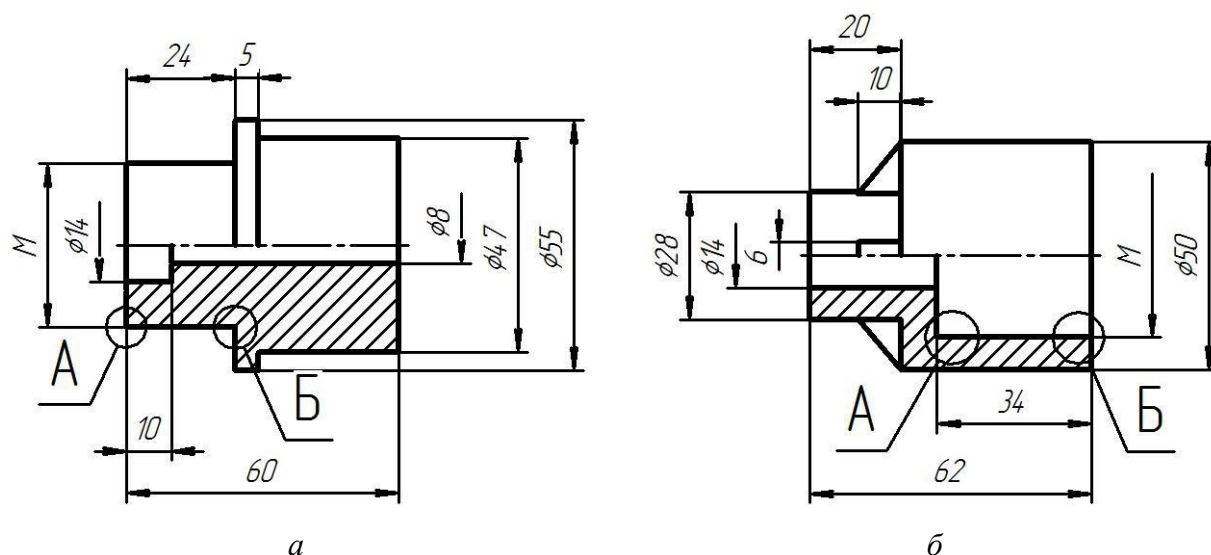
Конструкция деталей, входящих в состав резьбового соединения:
